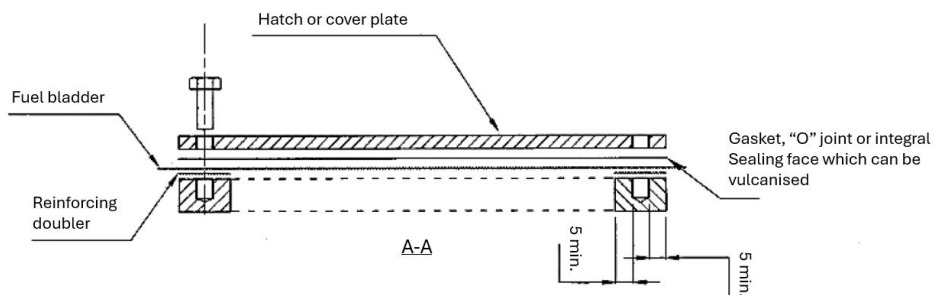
A - Anneau avec boulons pour vessie / Bolt ring for Bladder
